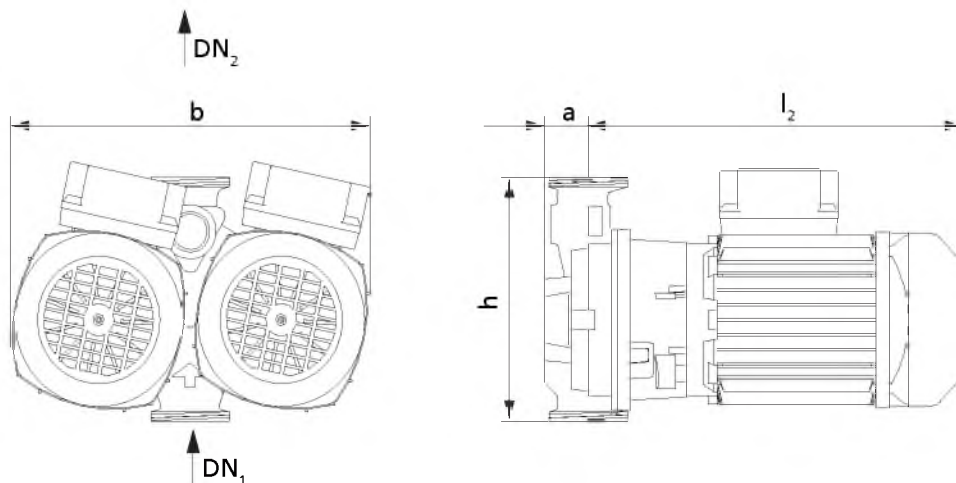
Размеры насосного агрегата с резьбовым соединением, типоразмер 032-032-080
